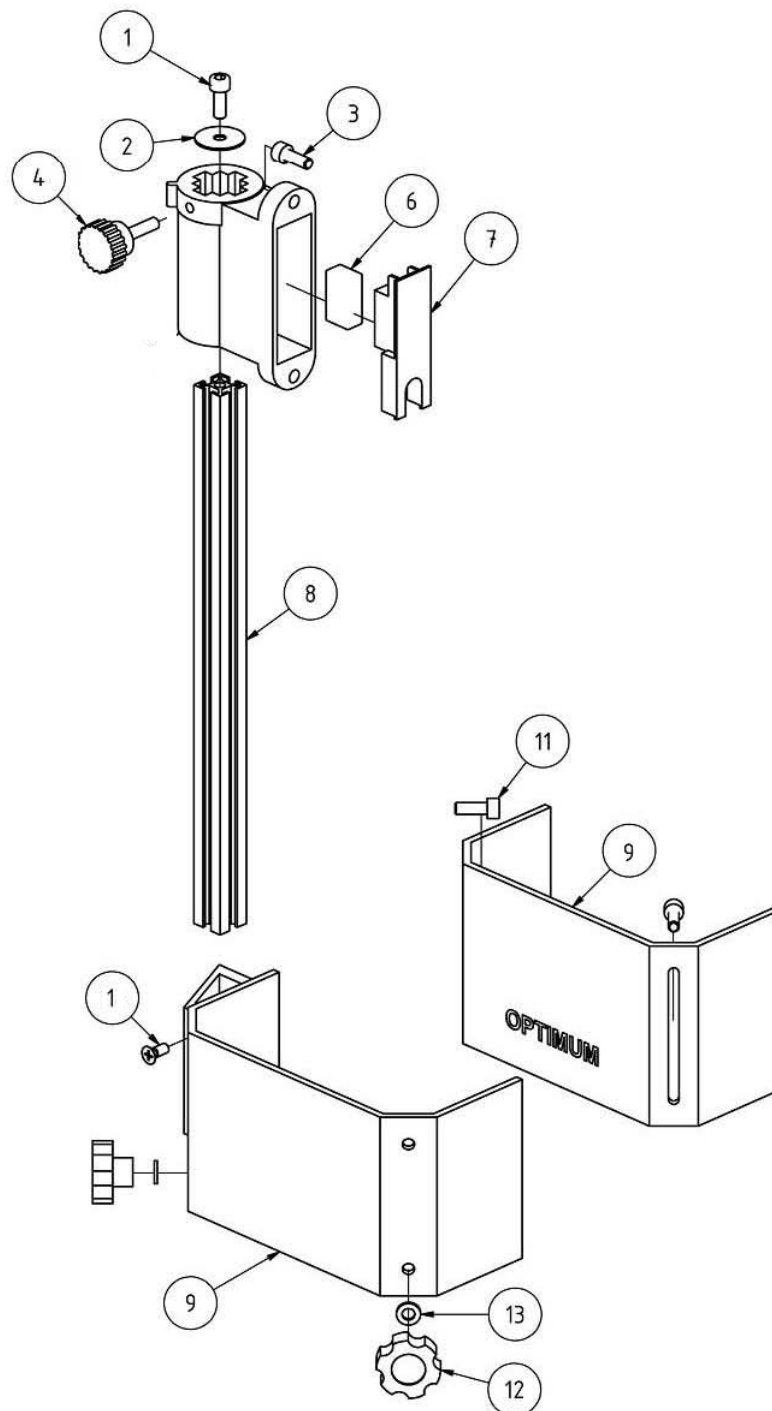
Bohrfutterschutz - Drill chuck protection
